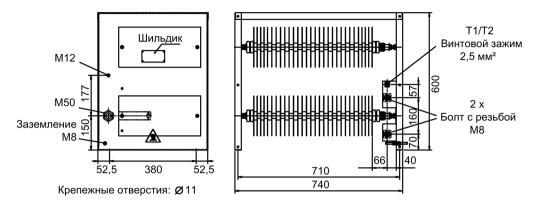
Габаритный чертеж тормозного резистора 25 кВт / 125 кВт
